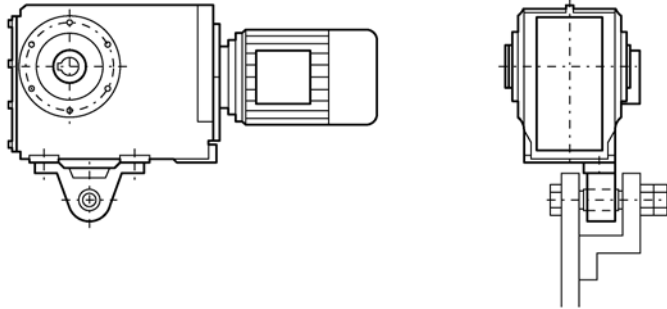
Montagevorschlag für Drehmomentstütze am Fuß
